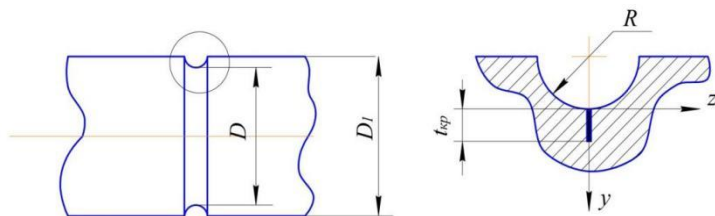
Цилиндрический образец с надрезом полукруглого профиля и нераспространяющаяся трещина усталости
